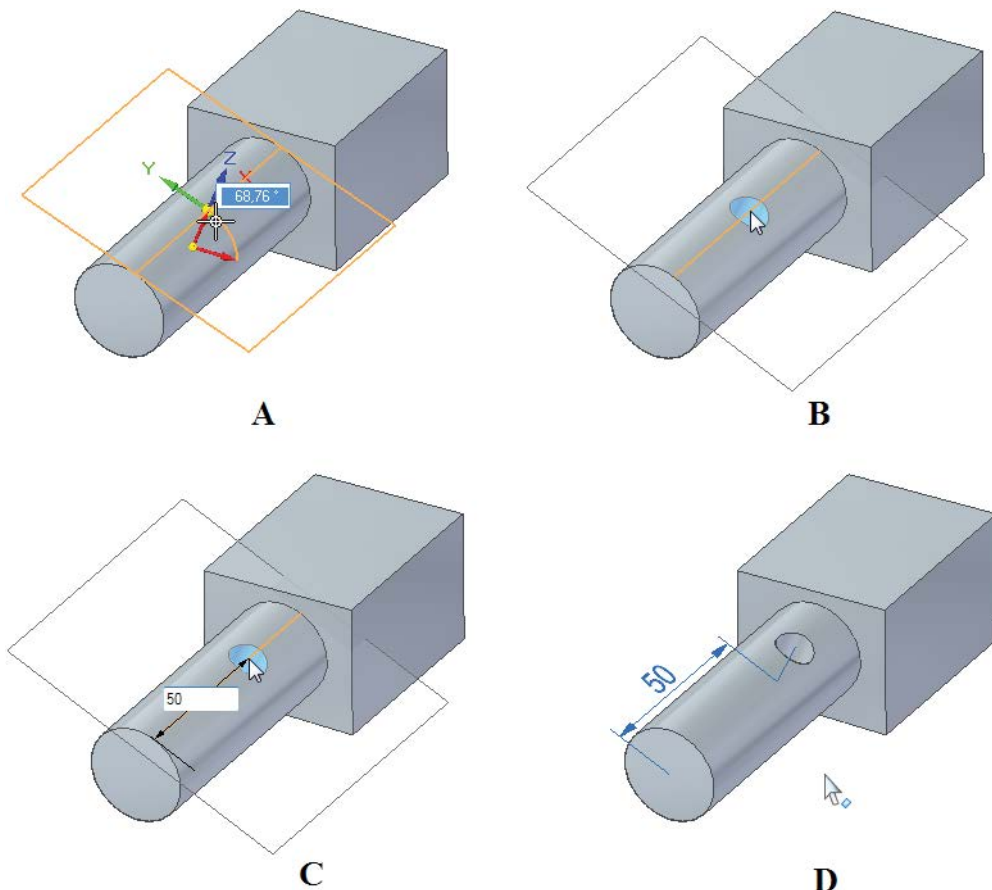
Процедура построения отверстия в цилиндрической поверхности
